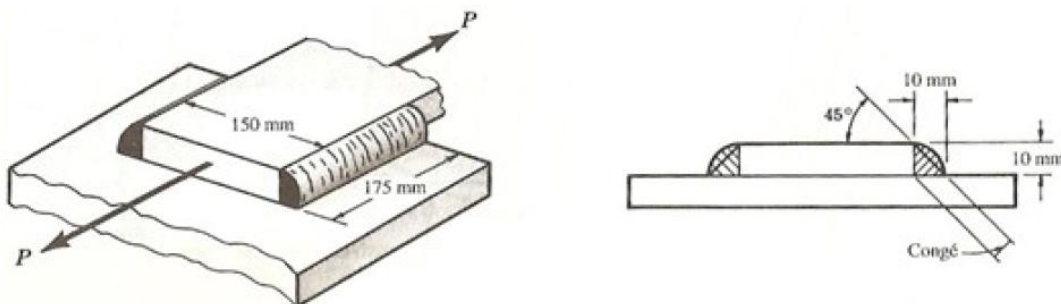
Exemple d'une soudure d'angle.
